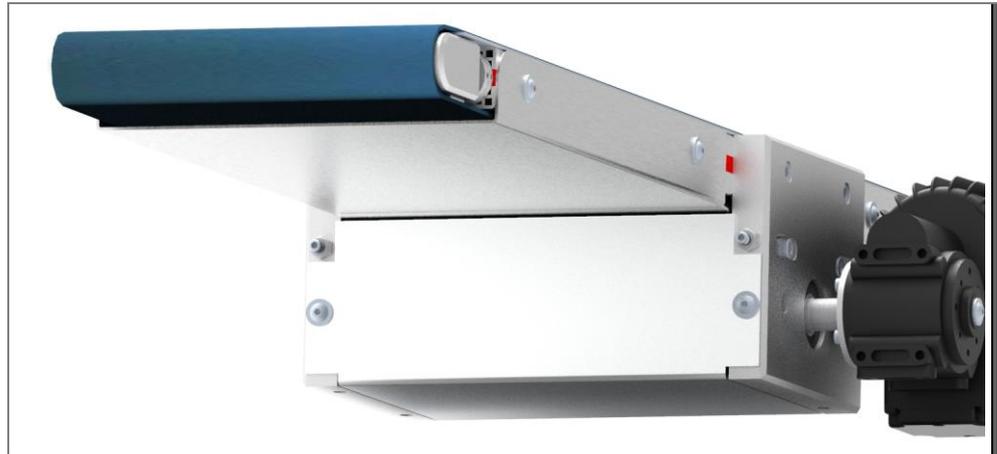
Beispielbild einer Standard-Rückführwanne mit Mittenmotor nach Zeichnungsnummer: M.800.0263
